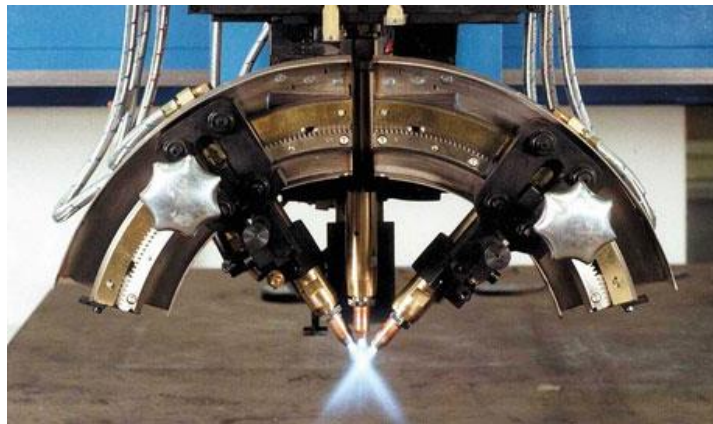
Triple Torch Unit D/KS /Messer cutting System, 2017/
